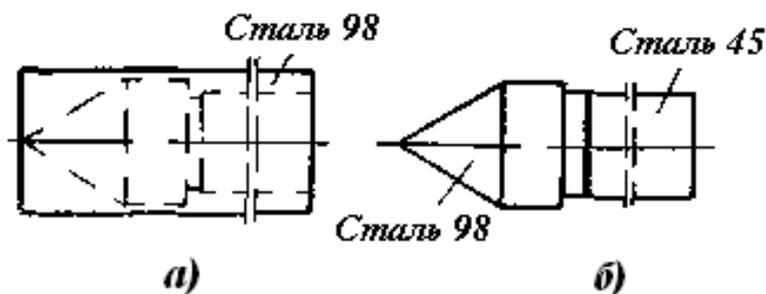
Изготовление валиков вращающихся центров по старой технологии (а) и с применением сварки трением (б)
